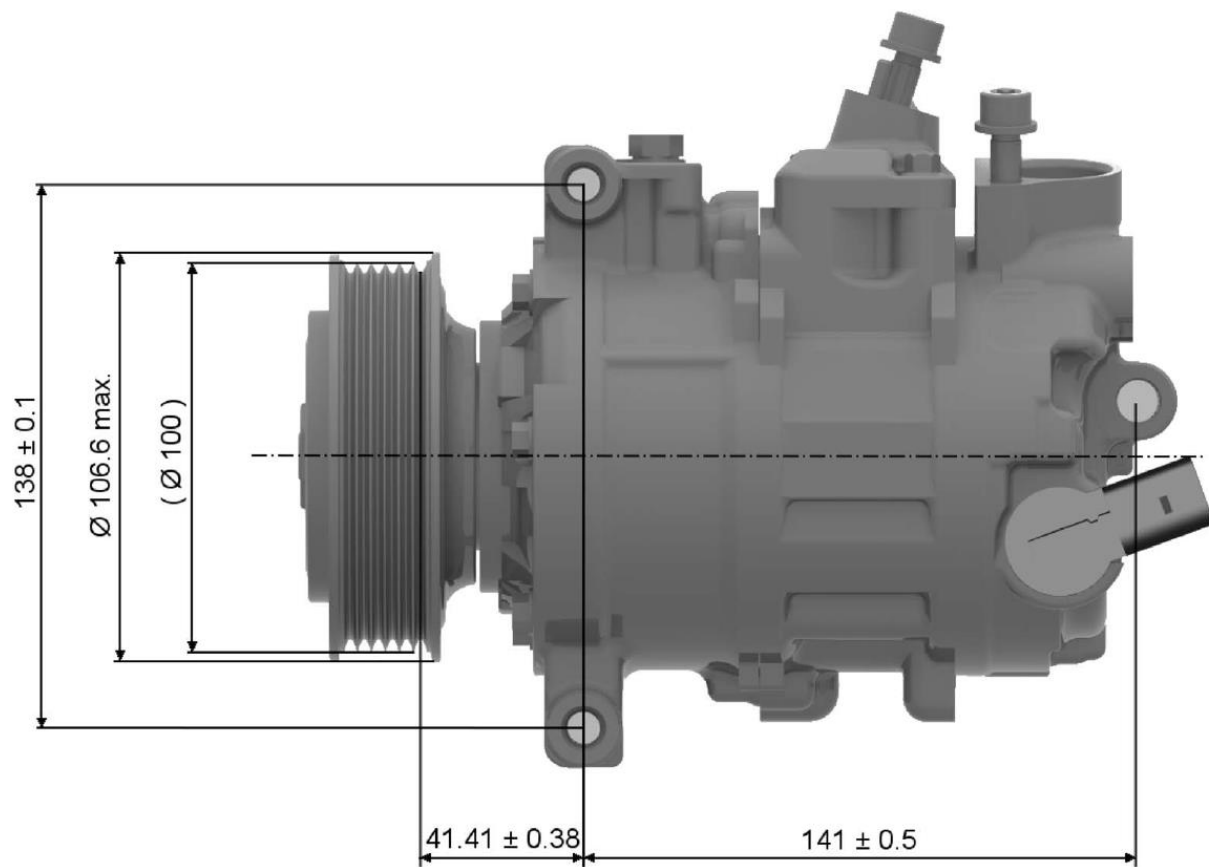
Abmessungen Klimakompressor, Scheibendurchmesser 100mm (Seitenansicht)
